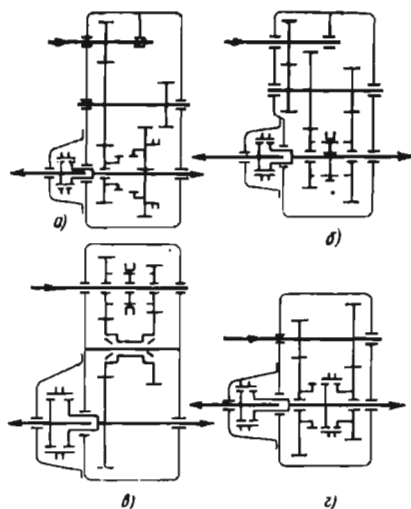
Схемы раздаточных коробок с блокированным приводом и соосными ведомыми валами автомобилей:
